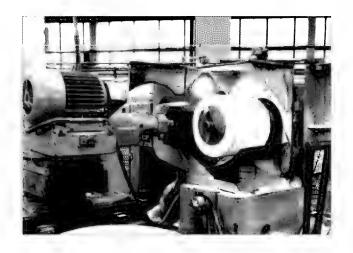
Общий вид токарно-лобового станка модели РТ-102 для обработки периферии круга
